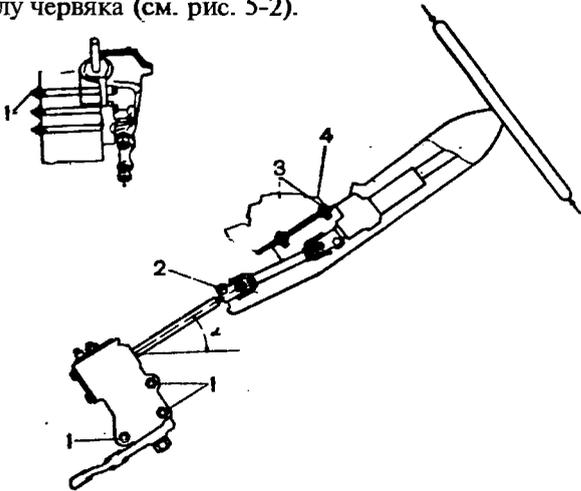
Установка рулевого механизма на автомобиль: 1 - болты крепления картера рулевого механизма; 2 - стяжной болт нижнего конца промежуточного вала; 3 - болты крепления кронштейна; 4 - кронштейн вала рулевого управления; 27,5 мм - расстояние от центра отверстия сошки до опорной поверхности картера рулевого механизма при среднем положении сошки
